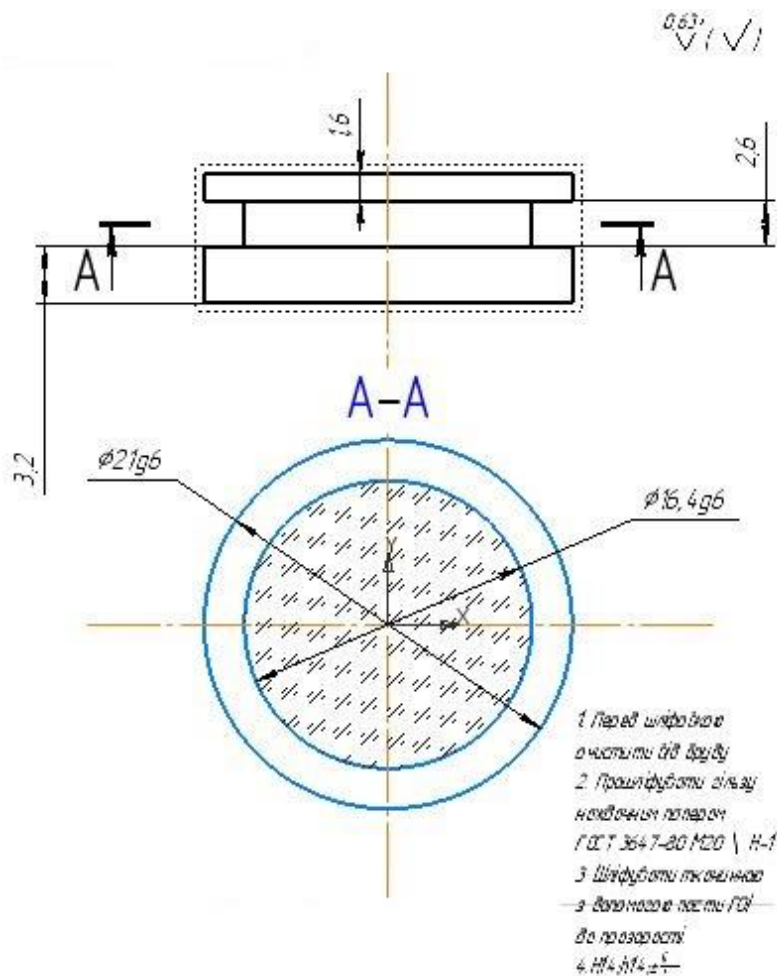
Кресленик плаваючого поршня демпфера
